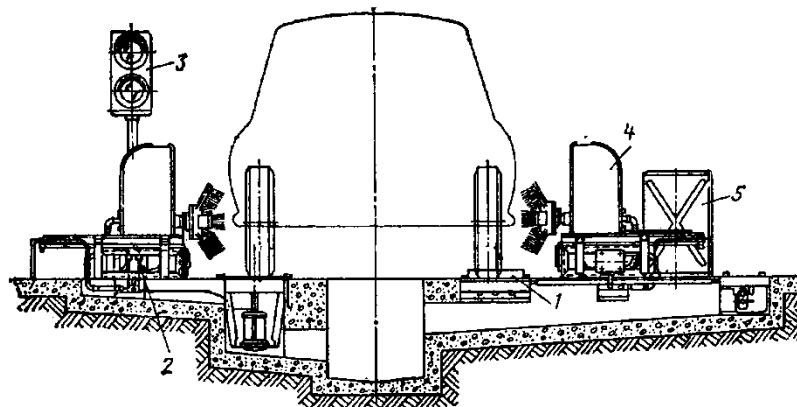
Установка для мойки колёс легковых автомобилей.
